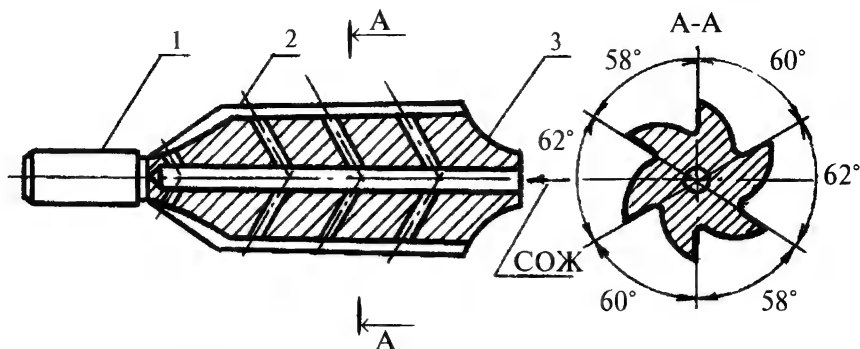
Шестизубая развертка для обработки конусов патронника: 1 - направляющая, 2 - режущая часть, 3 - хвостовик
